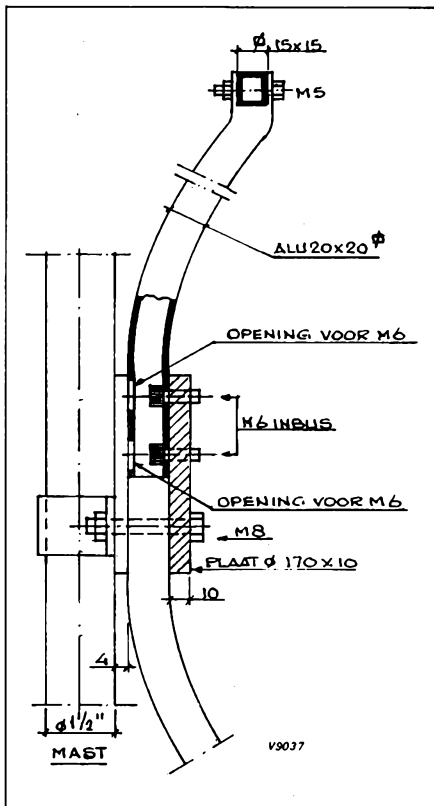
Detail van de bevestiging van de parabool. De constructie is gemaakt van vierkante aluminium pijp. Het geheel is gemonteerd op een ronde aluminium plaat van 10 mm dik.
